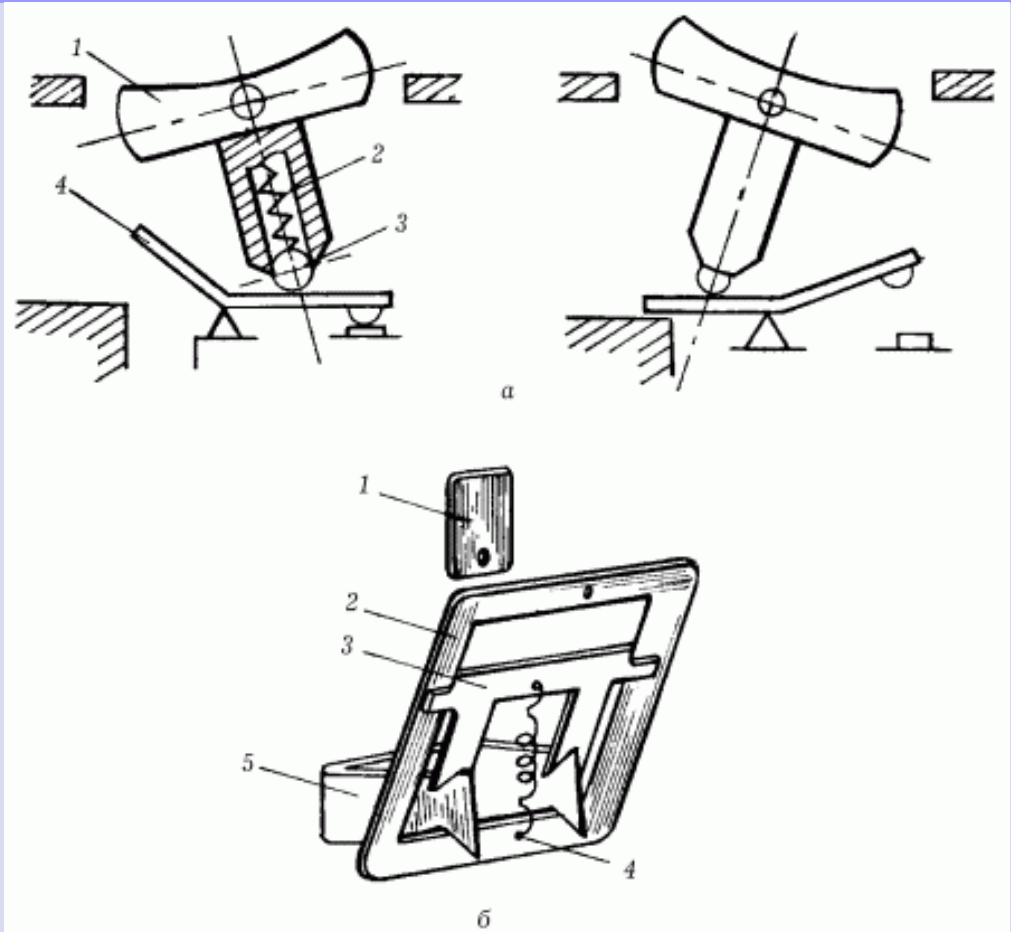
Конструкция механизмов выключателей: а – качающийся механизм выключателя с пружиной сжатия: 1 – клавиша; 2 – пружина; 3 – шарик; 4 – коромысло; б – качающийся механизм выключателя с пружиной растяжения: 1 – контактная пластина; 2 – рамка; 3 – скоба; 4 – пружина; 5 – основание.
